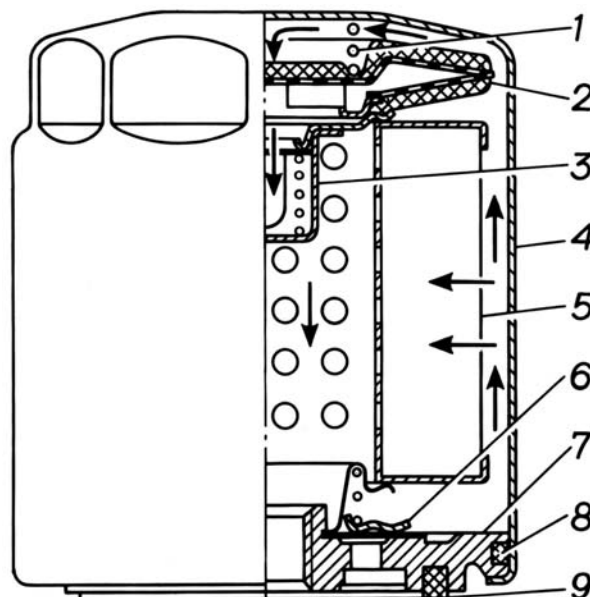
Масляные фильтры «БИГ-фильтр» и «КОЛАН»: 1 - пружина; 2 - фильтрующий элемент перепускного клапана; 3 - перепускной клапан; 4 - корпус; 5 - фильтрующий элемент; 6 - противодренажный клапан; 7 - крышка; 8 и 9 - прокладки
